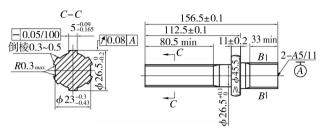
某型轿车变速器渐开线花键轴 Fig. 5 An involute spline shaft of a car's gearbox
